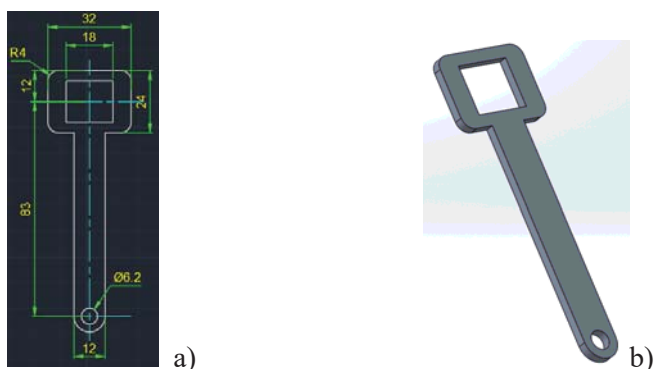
a) Proiectarea elementului 2 în format 2D, b) Elementul 2
